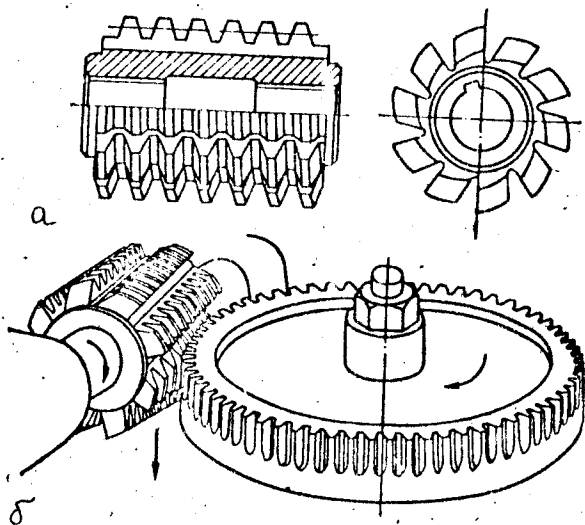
Нарізування зуб"ів черв"ячною фрезою
